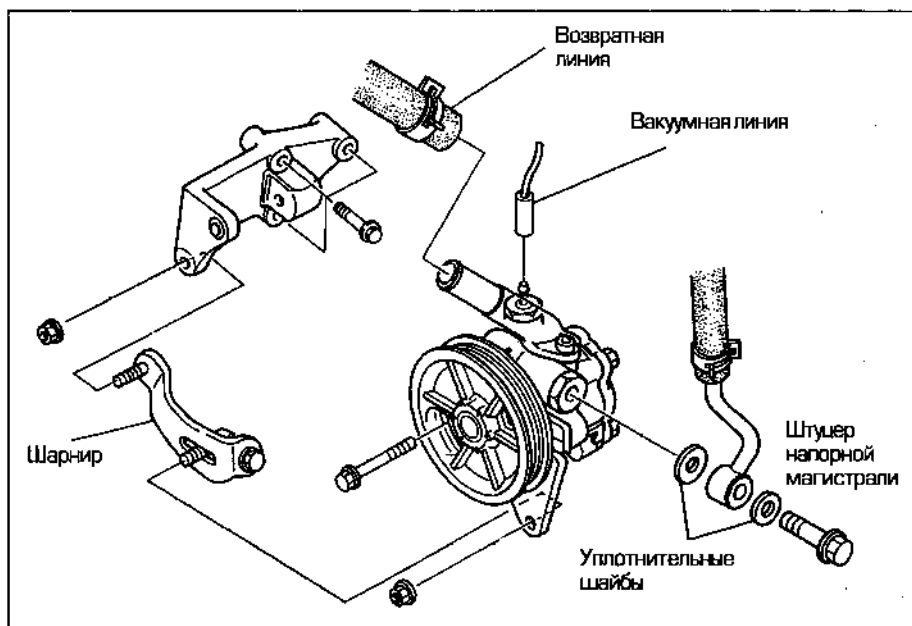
,б. Отсоедините возвратный шланг, штуцер напорной магистрали и вакуумный шланг
